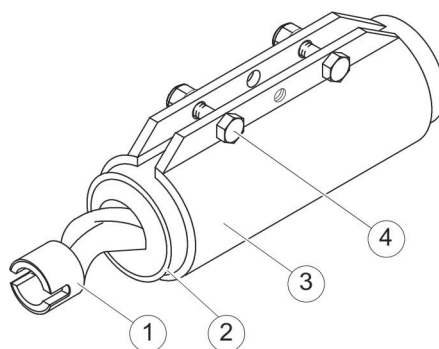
Vue d'ensemble de la pompe à vis avec gaine de serrage
